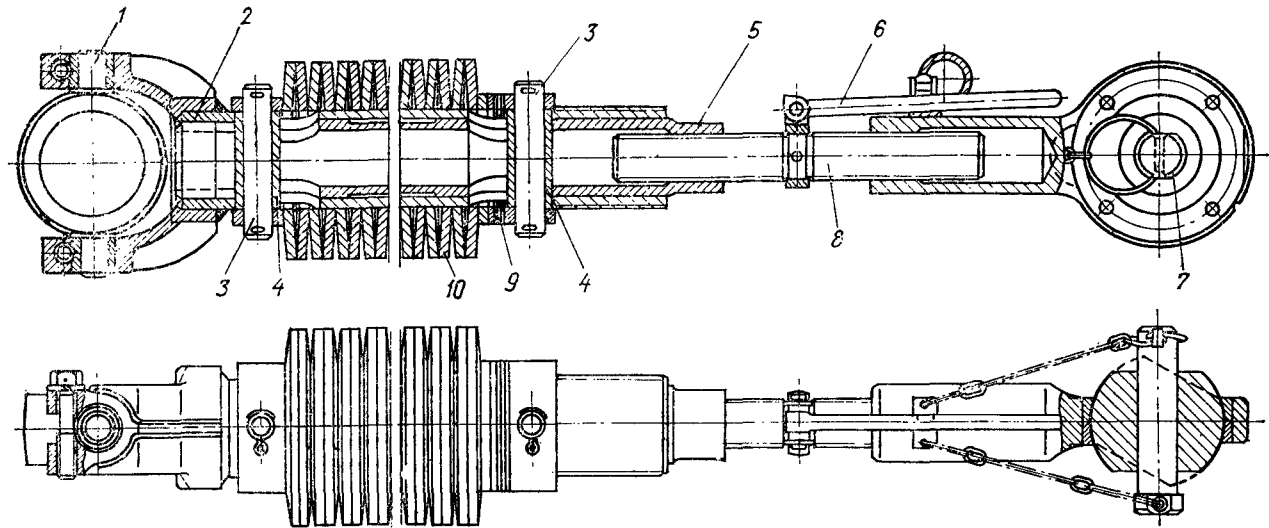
Верхняя тяга навесного механизма трактора К-701:
